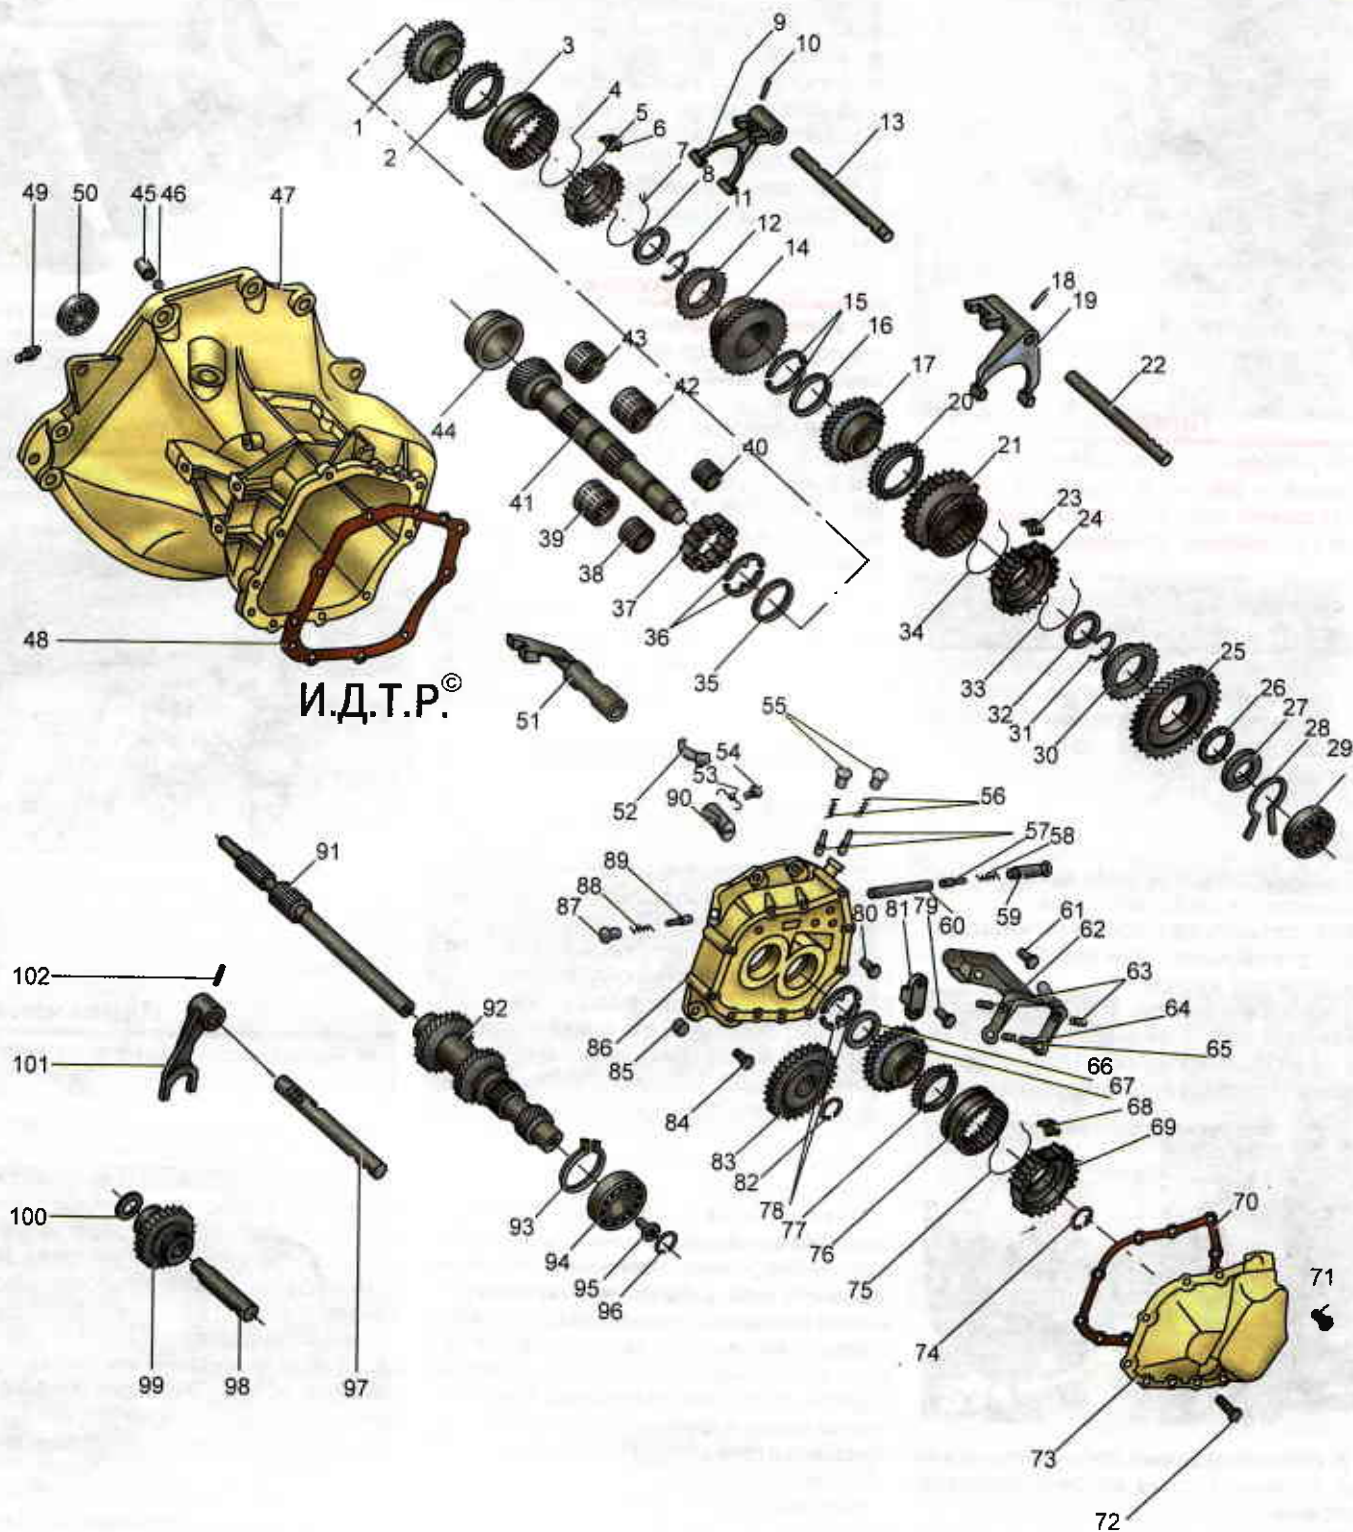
Детали механической коробки передач D-16: 1 – шестерня IV передачи; 2, 12, 20, 30, 77 – блокирующие кольца синхронизаторов; 3 – муфта включения синхронизатора III и IV передач; 4, 7, 33, 34, 75 – пружинные кольца синхронизатора; 5 – ступица синхронизатора III и IV передач; 6, 23, 68 – сухари синхронизатора; 8, 32 – упорные шайбы; 9 – вилка переключения III и IV передач; 10, 18, 102 – штифты; 11, 31, 74, 82, 93, 96 – стопорные кольца; 13 – шток вилки переключения III и IV передач; 14 – шестерня III передачи; 15, 36, 78 – упорные полукольца; 16, 35, 66 – залорные кольца; 17 – шестерня II передачи; 19 – вилка переключения I и II передач; 21 – муфта включения синхронизатора I и II передач; 22 – шток вилки переключения I и II передач; 24 – ступица синхронизатора I и II передач; 25 – шестерня I передачи; 26 – упорный игольчатый подшипник шестерни I передачи; 27 – опорная шайба; 28 – пружинное кольцо; 29 – подшипник вторичного вала; 37 – роликовый подшипник вторичного вала; 38 – игольчатый подшипник шестерни I передачи; 39 – игольчатый подшипник шестерни II передачи; 40 – игольчатый подшипник шестерни V передачи; 41 – вторичный вал; 42 – игольчатый подшипник шестерни III передачи; 43 – игольчатый подшипник шестерни IV передачи; 44 – наружное кольцо роликового подшипника вторичного вала; 45 – пробка; 46 – магнит; 47 – картер коробки передач; 48 – прокладка картера сцепления; 49 – выключатель фонарей заднего хода; 50 – роликовый подшипник первичного вала; 51 – поводок со штоком V передачи; 52 – собачка; 53 – пружина собачки; 54, 61, 71, 72, 79, 81, 84 – болты; 55, 59, 87 – пробки фиксаторов; 56, 58, 88 – пружины; 57, 89 – фиксаторы; 60 – штифт механизма блокировки; 62 – кронштейн вилки включения 5-й передачи; 63 – ось вилки включения V передачи; 64 – прокладка крышки; 65 – сухари вилки; 67 – ведомая шестерня V передачи; 69 – ступица синхронизатора V передачи; 70 – прокладка крышки; 73 – задняя крышка коробки передач; 76 – муфта включения синхронизатора V передачи; 80 – кронштейн собачки; 83 – ведущая шестерня V передачи; 85 – магнит; 86 – промежуточный картер; 90 – кронштейн собачки; 91 – первичный вал; 92 – блок шестерен; 94 – шариковый подшипник блока шестерен; 95 – винт; 97 – шток вилки включения промежуточной шестерни заднего хода; 98 – ось промежуточной шестерни заднего хода; 99 – промежуточная шестерня заднего хода; 100 – шайба; 101 – вилка включения промежуточной шестерни заднего хода
